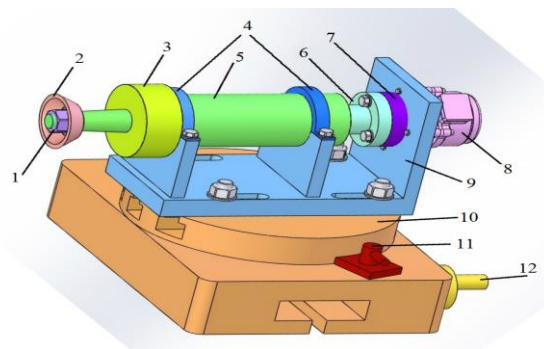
Приспособление для заточки режущего инструмента: 1 – гайка с шайбой; 2 – затачиваемый алмазный круг; 3 – подшипник; 4 – хомуты; 5 – шпиндель; 6 – полумуфта шпинделя; 7 – полумуфта электродвигателя; 8 – электродвигатель; 9 – основание; 10 – поворотный стол; 11 – откидные рукоятки; 12 – маховик.
